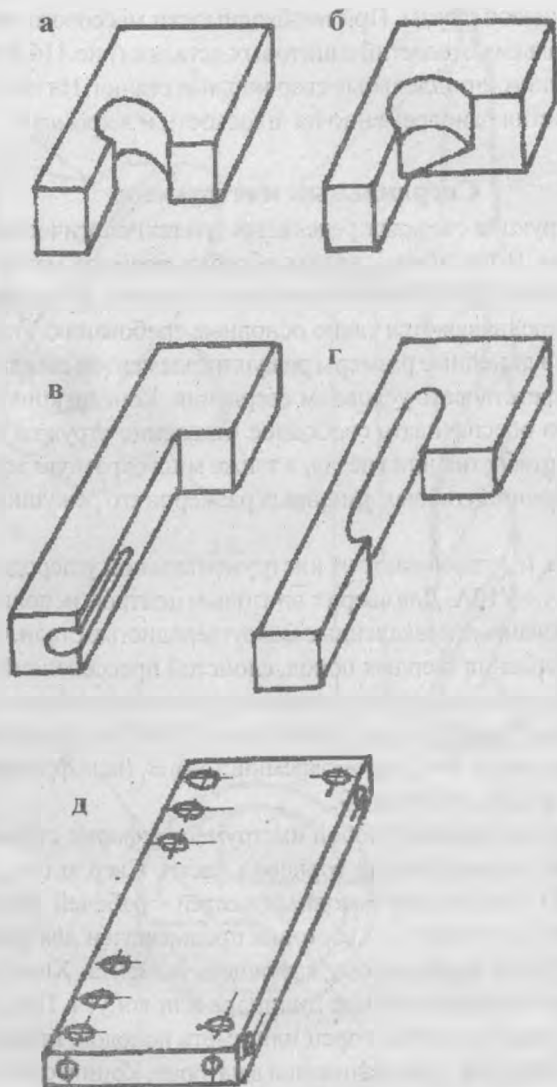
Виды работ, выполняемых на сверлильно-пазовальных и сверлильно-присадочных станках:
